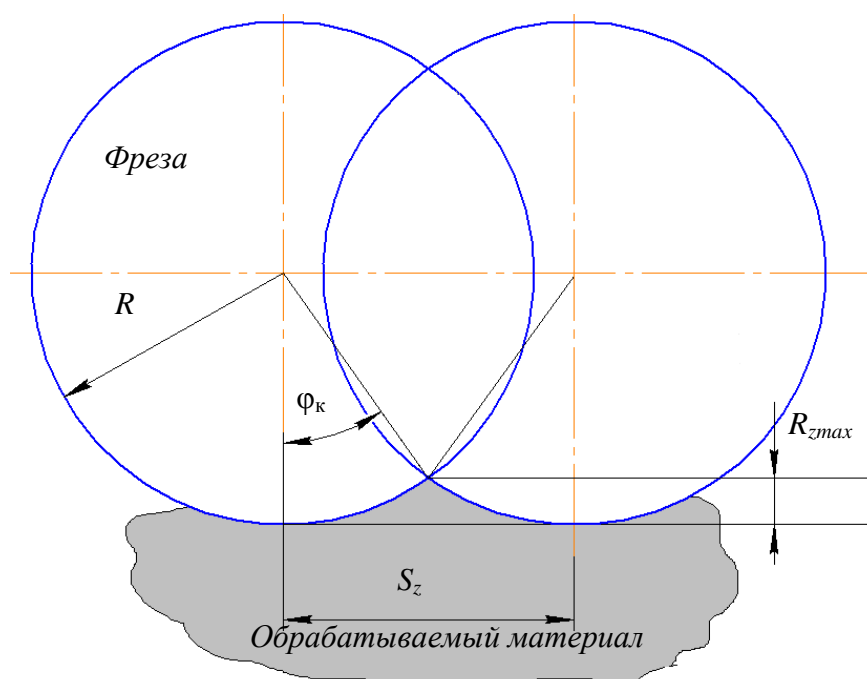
Расчетная схема процесса цилиндрического фрезерования
